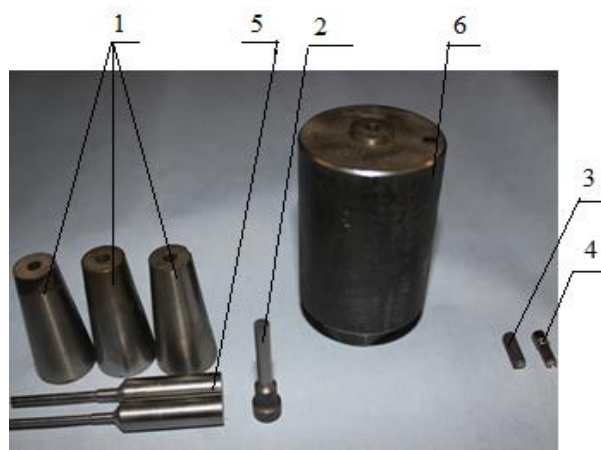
Инструментальная оснастка: 1 – матрица; 2 – пуансон; 3 – исходная заготовка; 4 – заготовка после деформации; 5 – выталкиватель; 6 – корпус для центрирования инструмента
